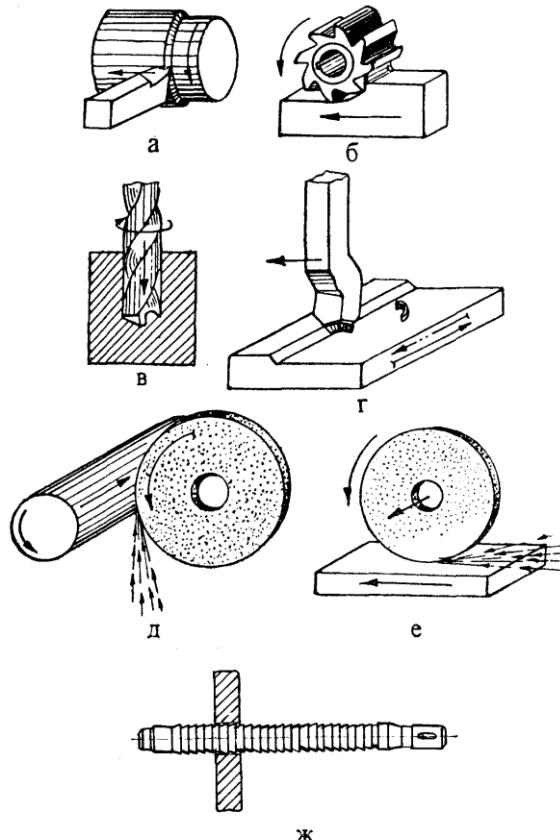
Схемы обработки заготовок резанием: *а* – точение; *б* – фрезерование; *в* – сверление; *г* – строгание; *д* – шлифование на круглошлифовальном станке; *е* – шлифование на плоскошлифовальном станке; *ж* – протягивание
